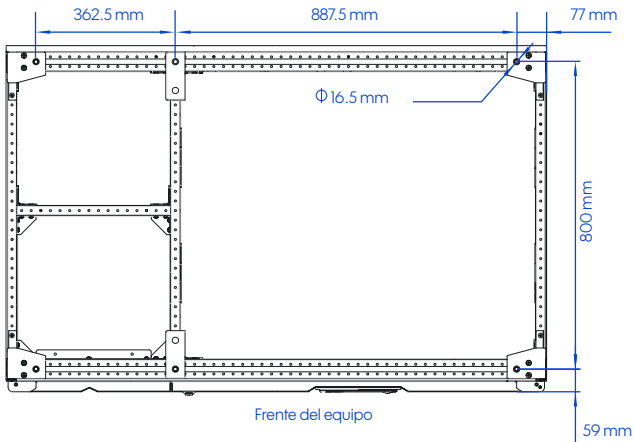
Dimensiones de instalación del pedestal del UPS-IND HF 13500 y 13600 (500 y 600 kVA)
